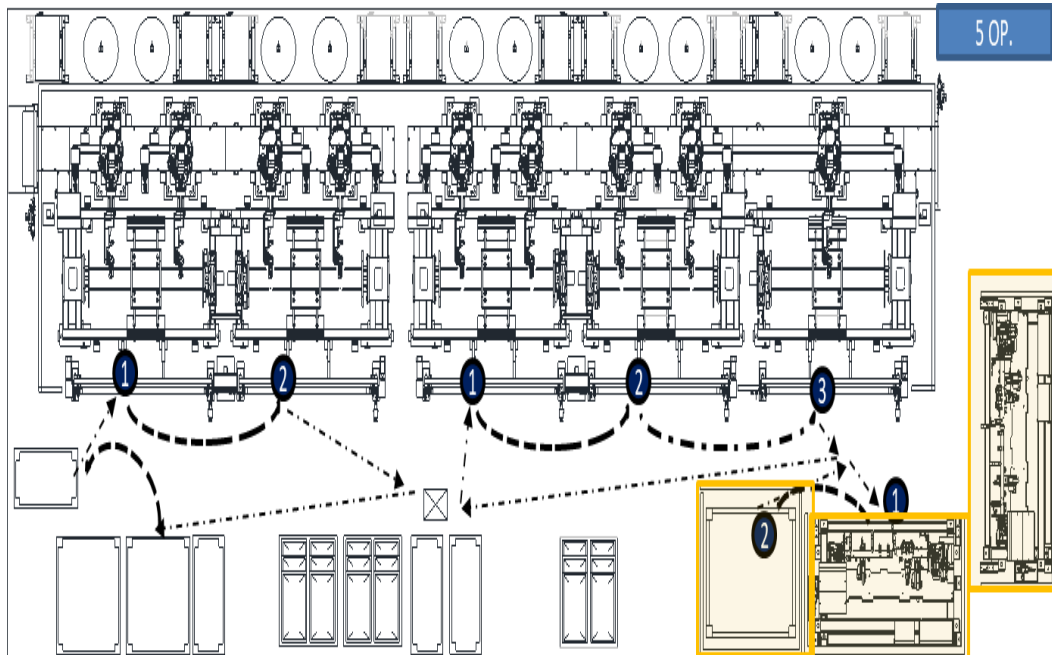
LAYOUT DE LINEA 678701HK1A
